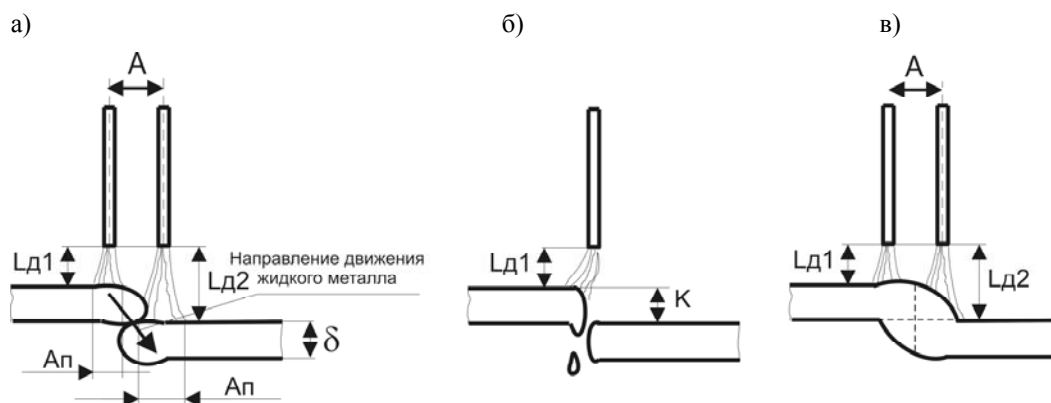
Схема, отражающая условия горения дуги при сварке соединений со смещением кромок: L_d – длина дуги; A_p – анодное пятно; A – размах колебаний
